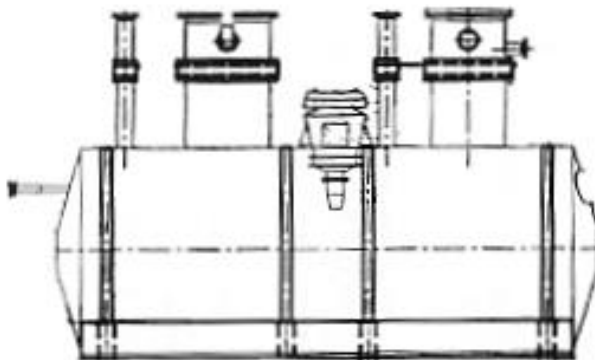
Общий вид эскиза резервуара РГС-16
